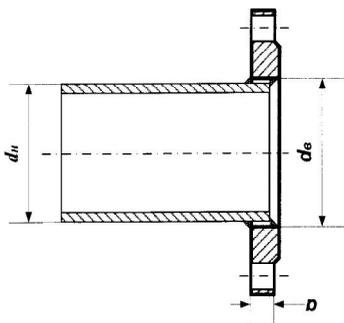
Конструкция и размеры стального плоского фланца по ГОСТ 12820-80 (к табл. 21)
